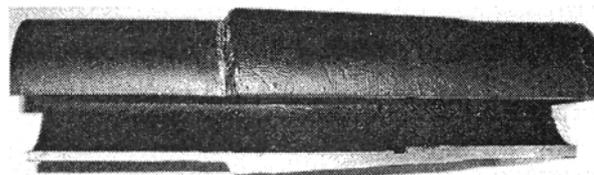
Сварное нахлестное соединение труб типа «НЗ»
